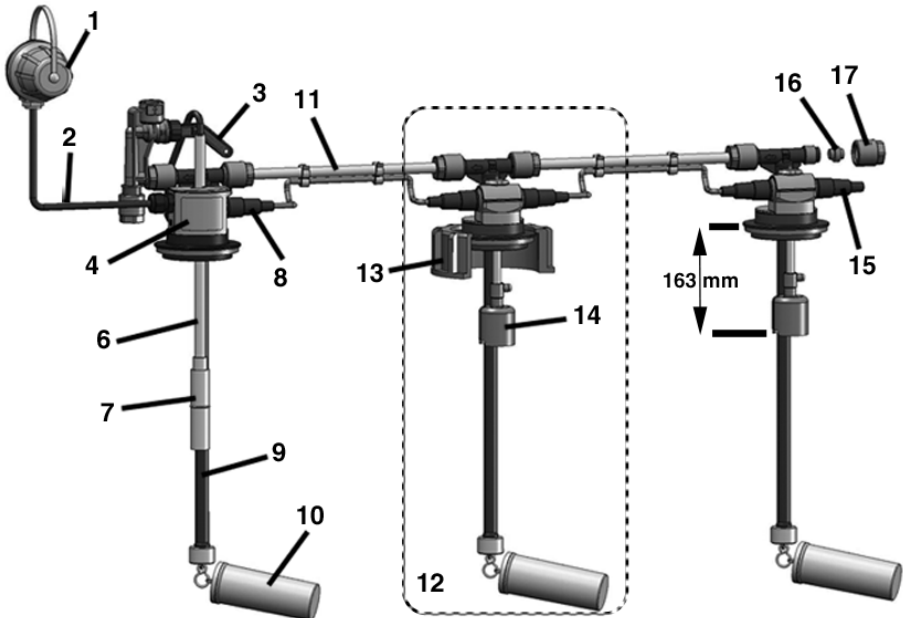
Grundeinheit mit GWG 12 K/14/NK-SWS und Erweiterung mit Schwimmerschalter
